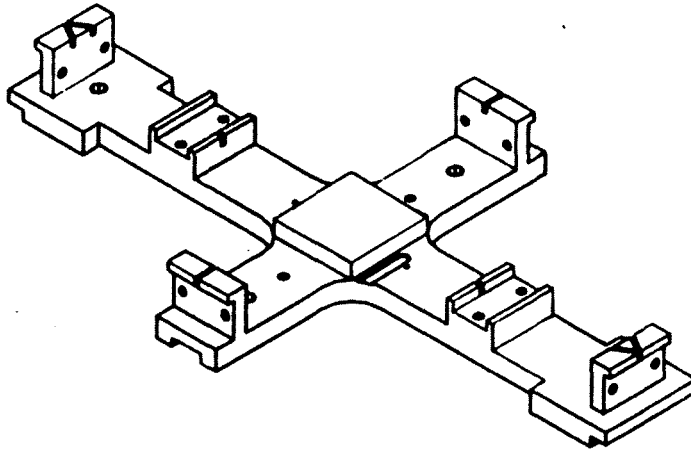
Drei-dimensionale Skizze eines der Module für sechs HALL-Proben.
